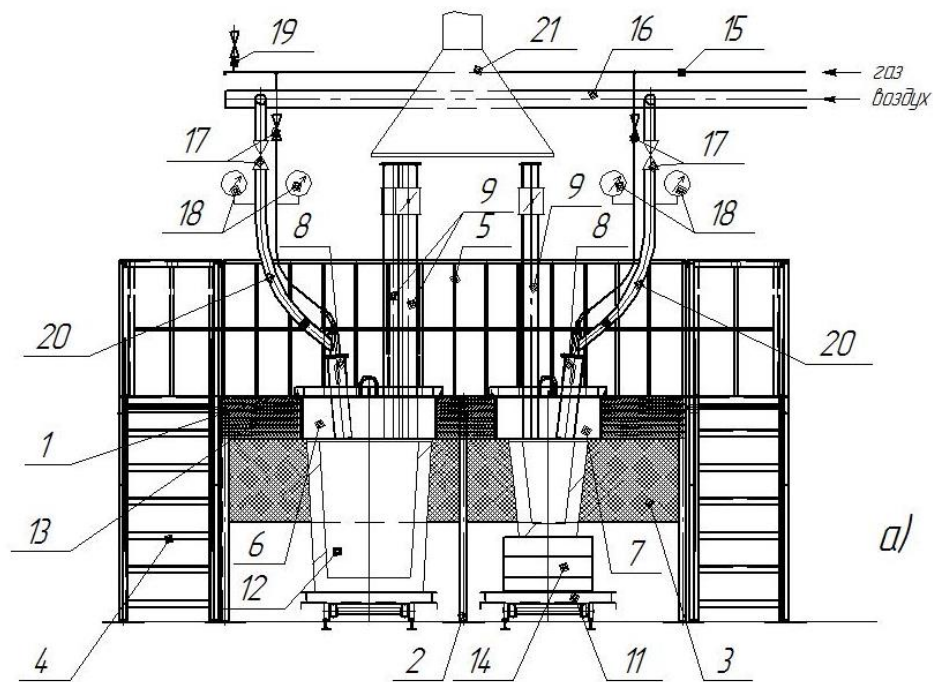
Общий вид станда для сушки и разогрева ковшей:
